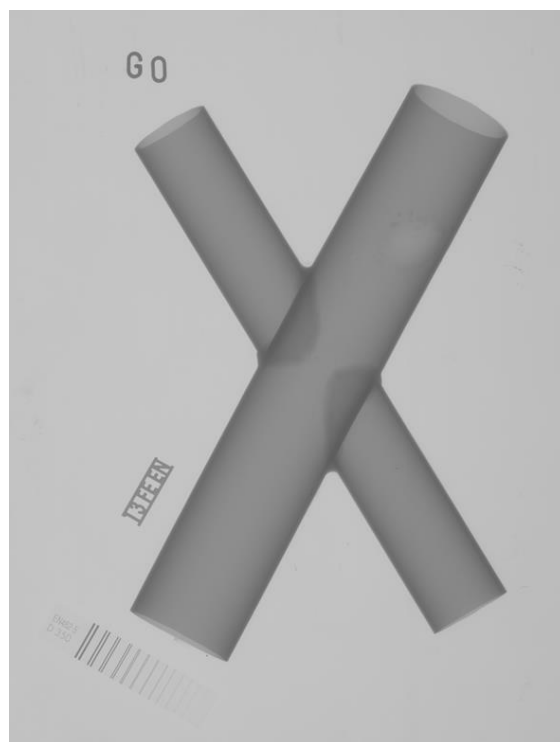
Segment šasije FIREWALL: stanje unutrašnje površine cijevi, detalji zavara
